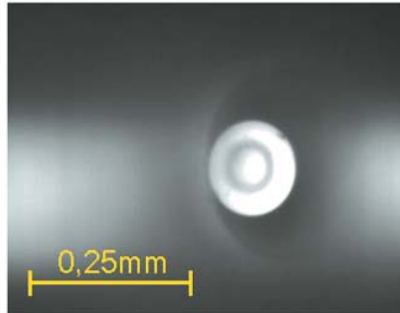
Fasertaster im Eigenleuchtmodus (Messung einer Einspritzdüse, Eintauchtiefe 0,6 mm)
